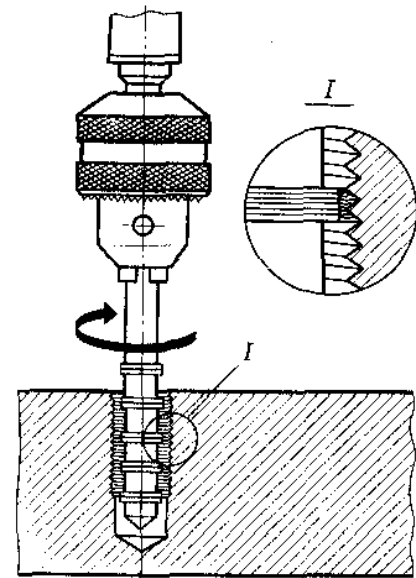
Очистка резьбовых отверстий от грязи ершом
